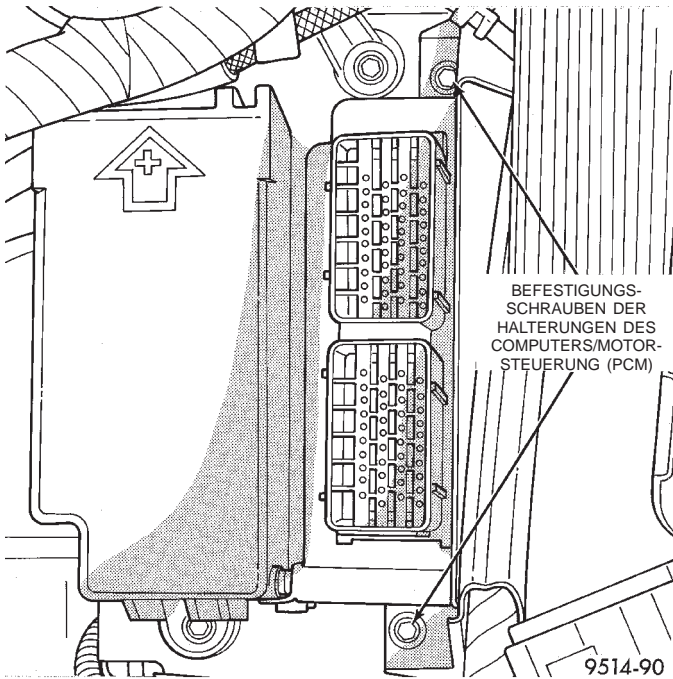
Befestigungsschrauben der Halterung des Computers/Motorsteuerung (PCM)
